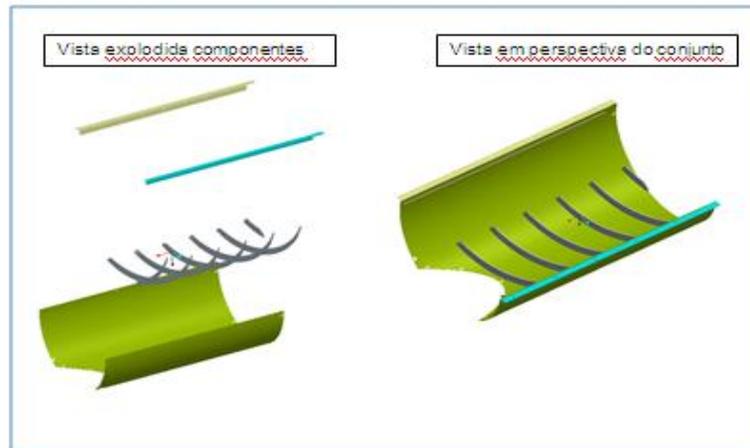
Conjunto soldado. Fonte: Pesquisa (2012)
